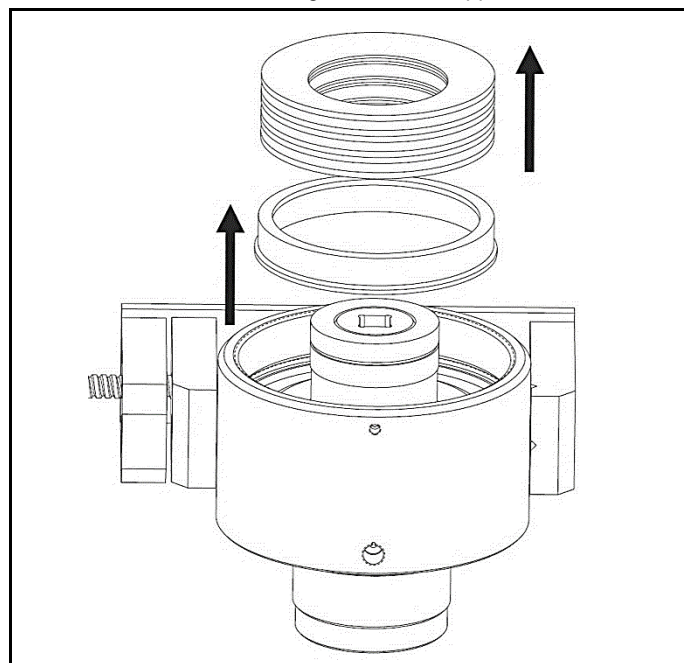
Tellerfedern und Federeinsatz entfernen.
